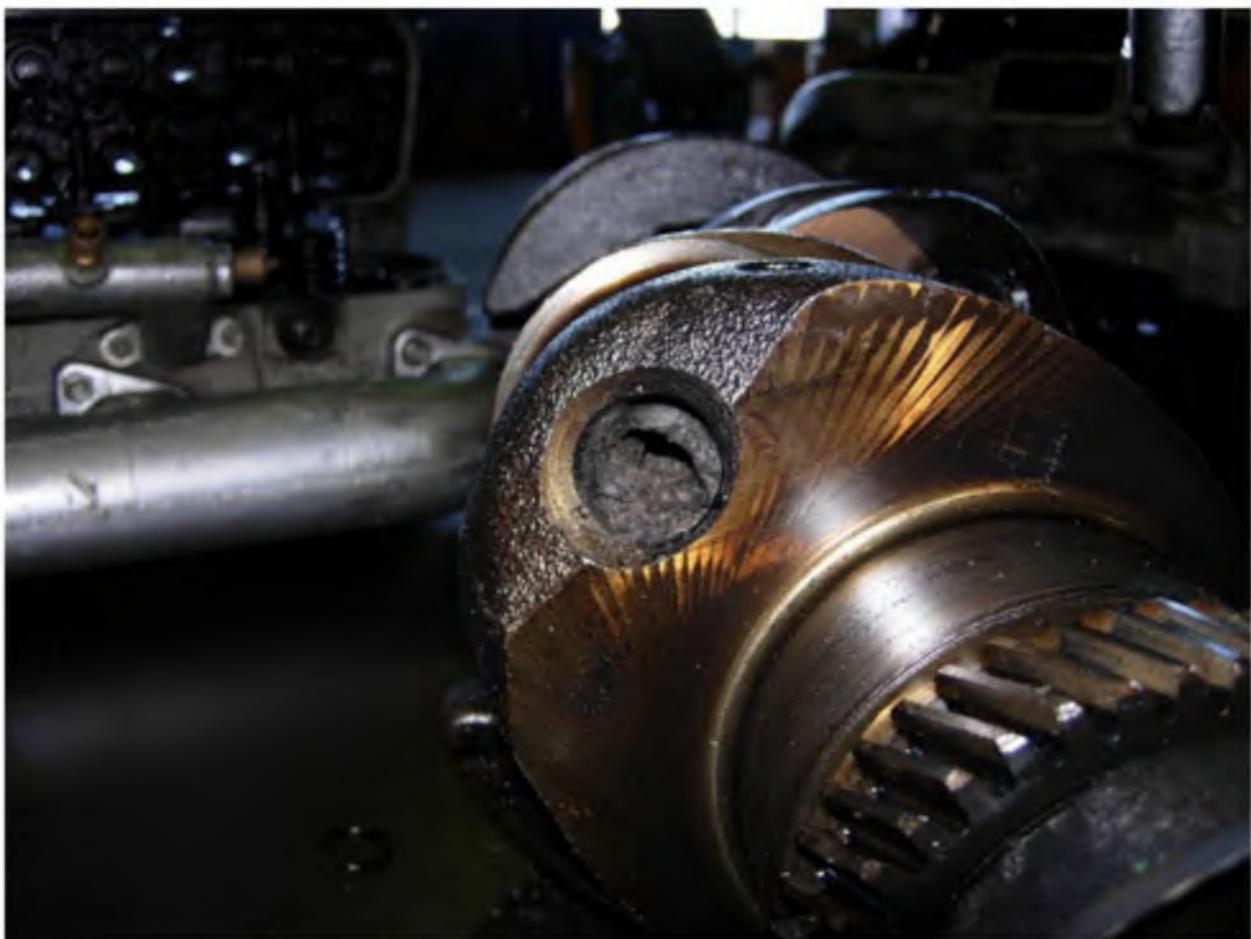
Отложения в ловушке коленчатого вала двигателя
